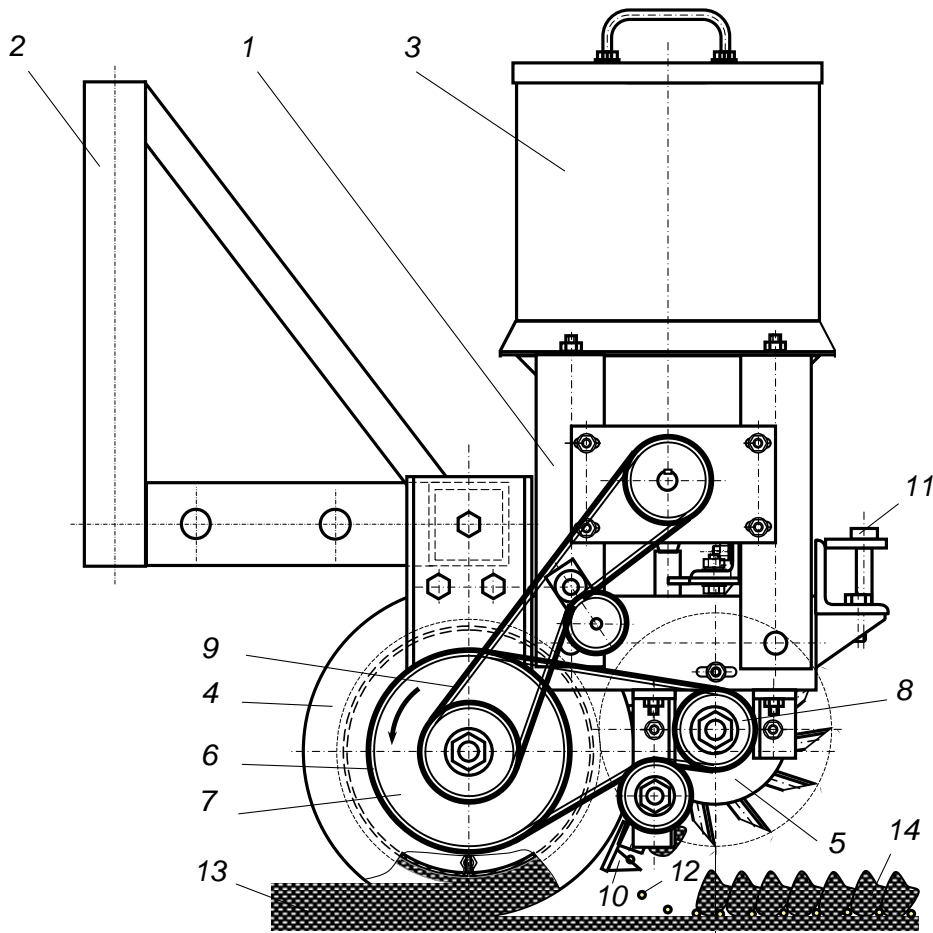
Сівалка-різак (вид з ліва): 1 – рама; 2 – начіпний пристрій; 3 – насінневий бункер; 4 – дисковий ротор; 5 – фрезерний ротор; 6 – ланцюговий привід фрезерного ротора; 7 і 8 – ведуча і ведома зірочки приводу фрезерного ротора; 9 – привід висівного апарата; 10 – висівач насіння; 11 – причіпний пристрій для агрегування котка; 12 – насіння; 13 – горішній зволожений шар ґрунту; 14 – дрібні грудки ґрунту, збиті лопатками фрезерного ротора.
